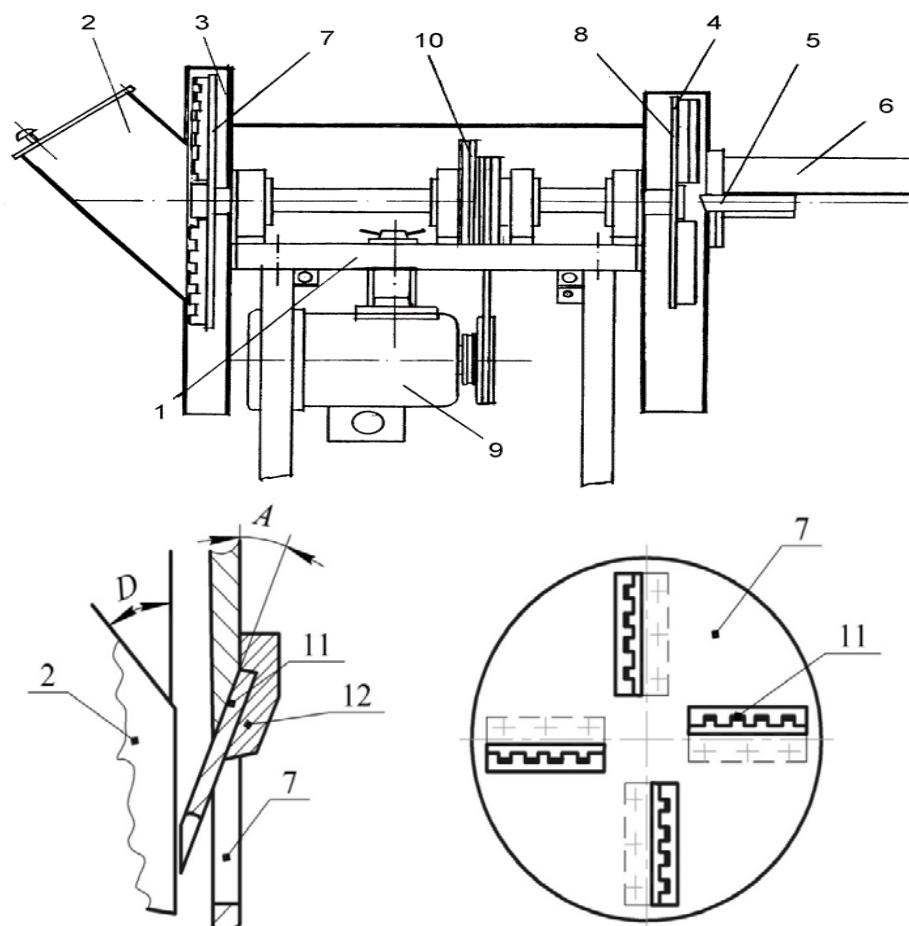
Измельчитель растительного сырья по патенту № 2 142 217: 1 – рама; 2 – загрузочный бункер; 3 – механизм резки корнеплодов; 4 – механизм резки трав; 5 – неподвижный нож; 6 – лоток; 7, 8 – диски; 9 – двигатель; 10 – клиноременная передача; 11 – ножи; 12 – накладка
